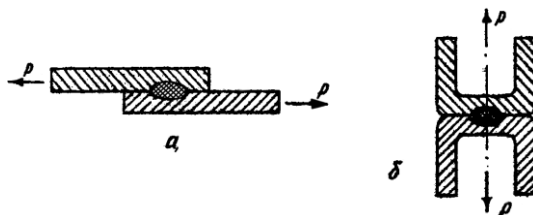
Схема испытания сварного соединения:
